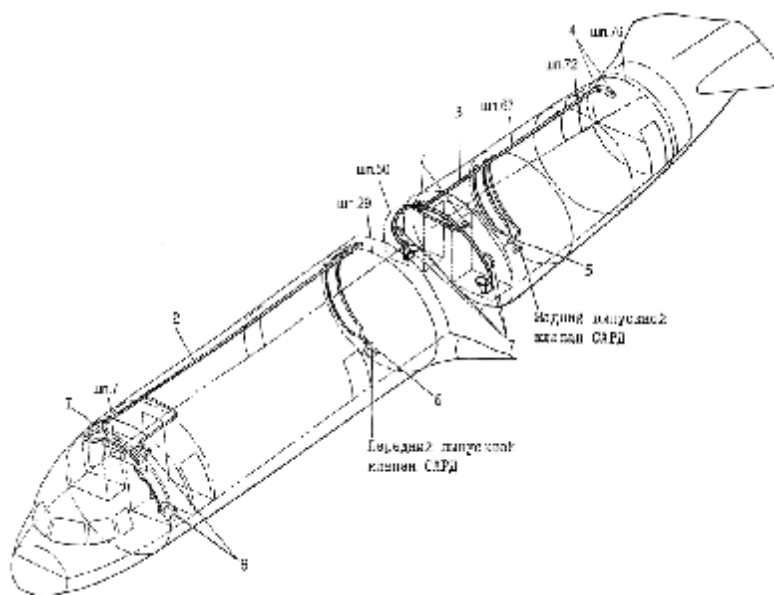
Размещение системы вытяжной вентиляции самолёта Ту-204-300 (сер. №044): 1 – вытяжной патрубков передней кухни; 2 – трубопровод вытяжки воздуха из передних бытовых помещений; 3 – трубопровод вытяжки воздуха из задних и средних бытовых помещений; 4 – вытяжной патрубков задней кухни; 5, 6 – вытяжной вентилятор 1,0 ЭВ-5,6-200-3661; 7 – вытяжной патрубков среднего туалета; 8 – вытяжной патрубков переднего туалета
